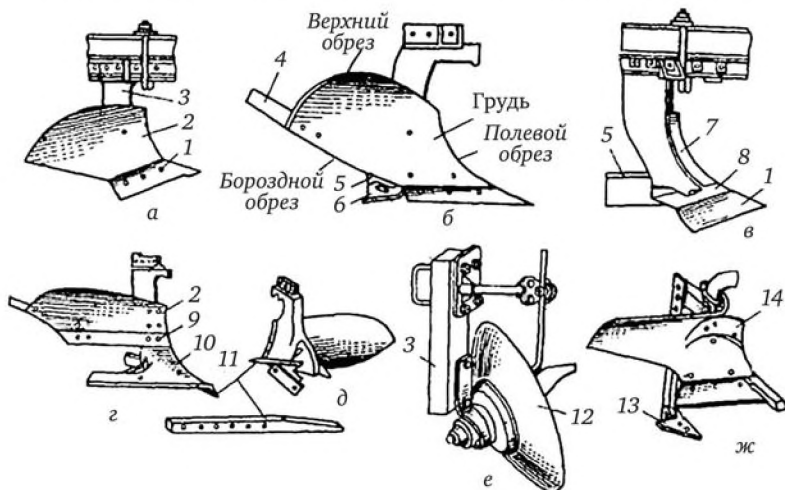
Современные корпуса плугов, используемые для вспашки старопахотных почв:
